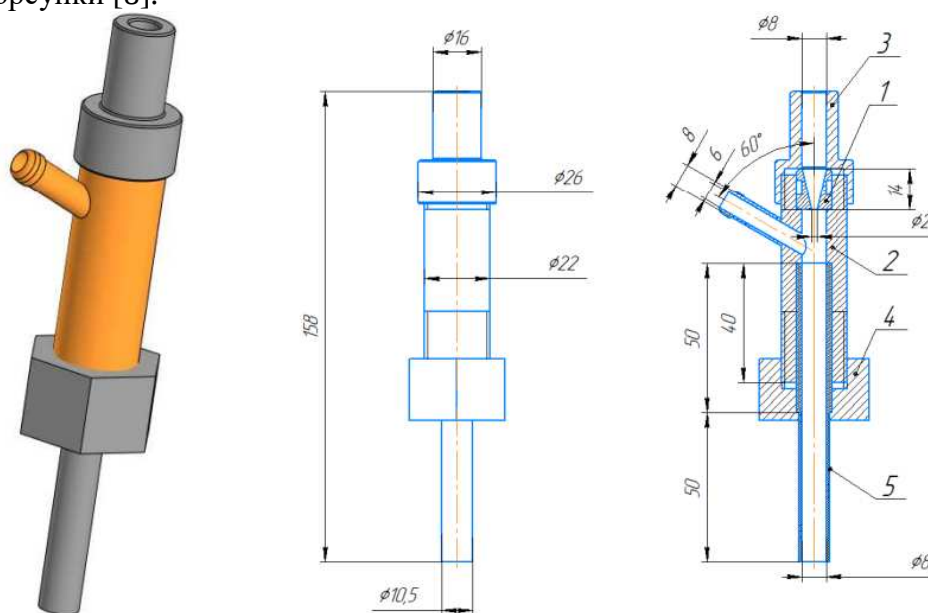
Гидроабразивный резак: 1 – форсунка; 2 – корпус; 3 – штуцер для подачи воды; 4 – гайка коллиматора; 5 – коллиматор
